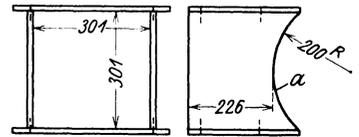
Kasten zum Stützenkern zu Fig. 156.
